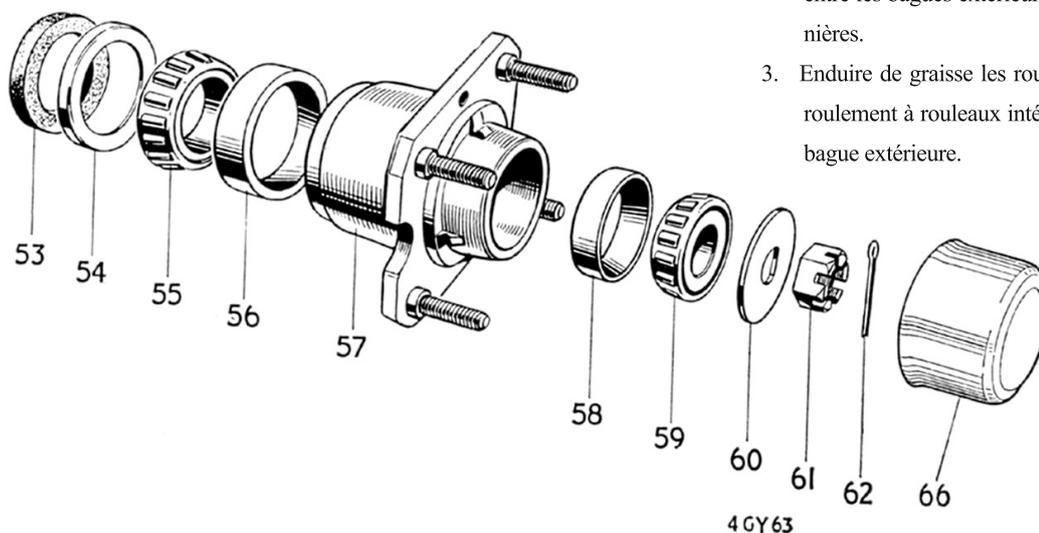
Vue éclatée des roulements du moyeu (modèle avec freins à tambour)
